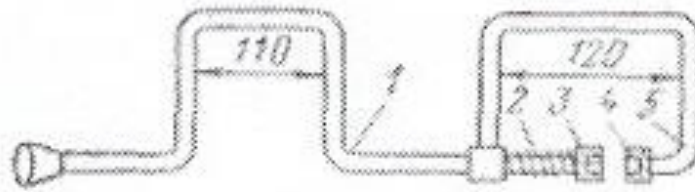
Приспособлення для розбирання і складання гальмівних камер:
